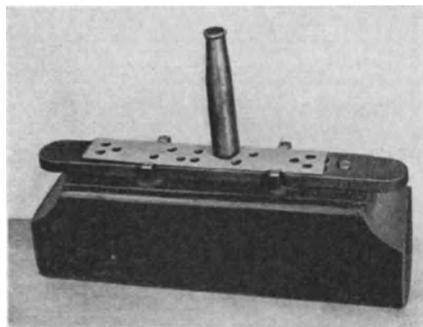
Schlagplatte zum Schlagen der Schaftkarten für Schaftmaschinen.
